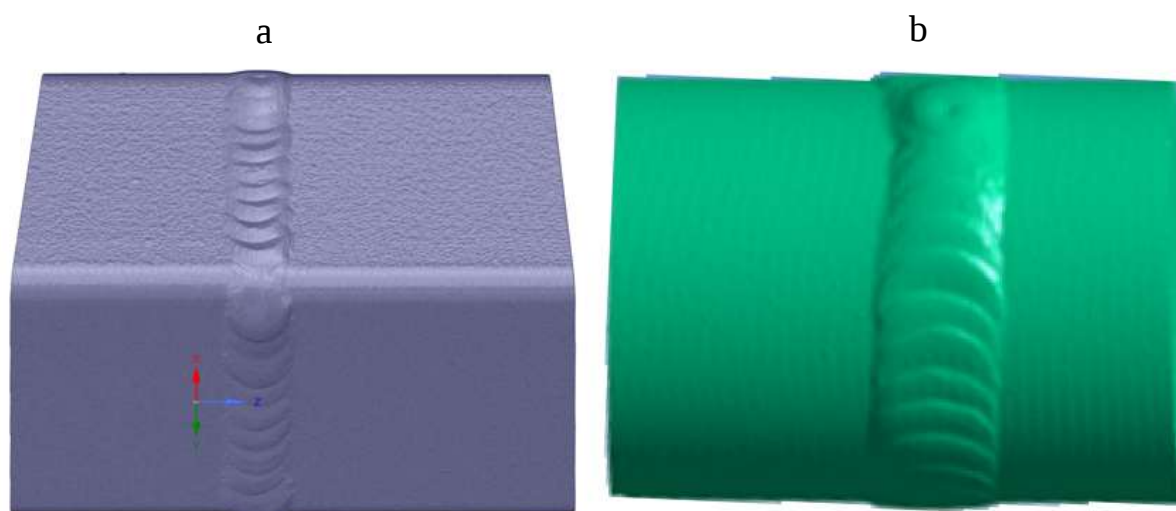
Scan 3D de deux cordons de soudure, réalisé sur des tubes carrés (a) et ronds (b) soudés bout à bout.
